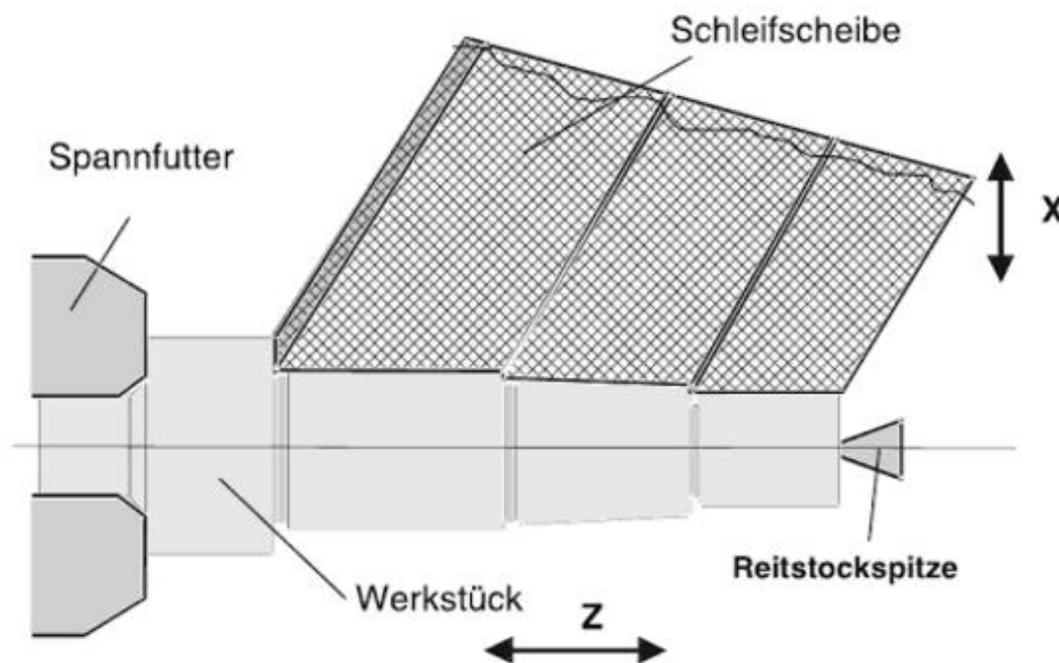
Arbeitsbeispiel einer Wellen-Komplettbearbeitung auf einer CNC-Schrägeinstech-Schleifmaschine mit einer durch eine Diamant-Abbrichtrolle profilierten Schleifscheibe^[7]
